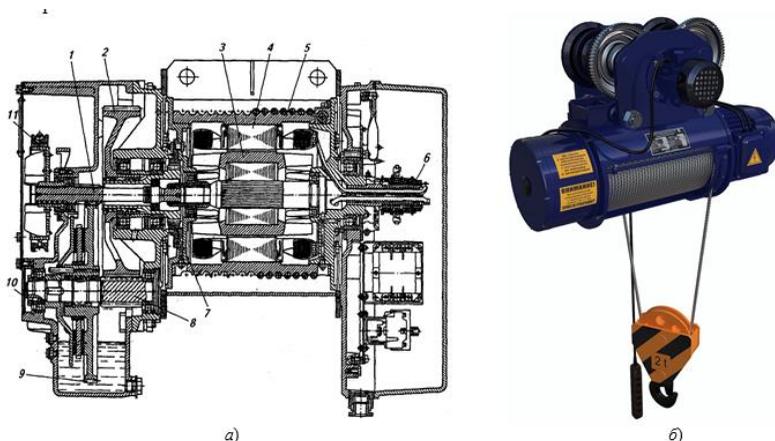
Электрическая таль с двигателем, встроенным в барабан: *а* – устройство: 1, 8 – шестерни; 2, 9 – зубчатые колеса; 3 – ротор; 4 – статор; 5 – барабан; 6 – кольцевой токоприемник; 7 – зубчатая муфта; 10 и 11 – винтовой и электромагнитный тормоза; *б* – общий вид
